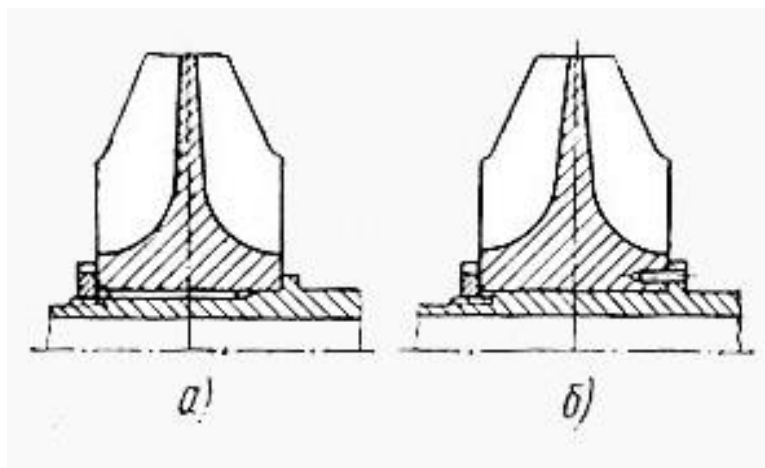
Способ передачи крутящего момента от вала к колесу:
